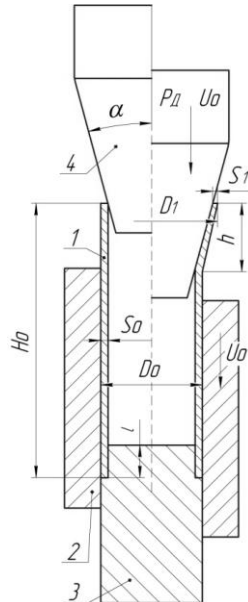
Схема закритої роздачі трубчастої заготовки
